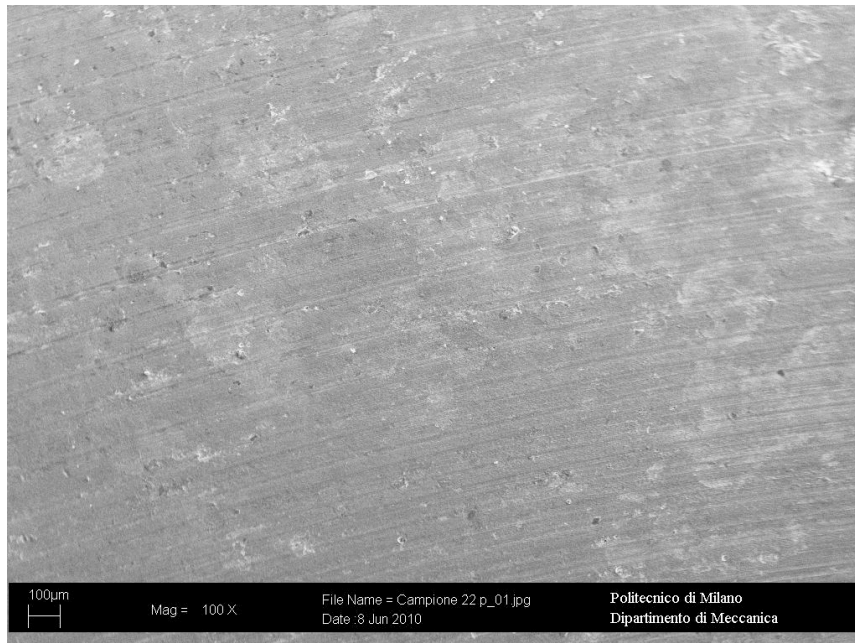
Immagine X100 (SOD=45 mm; f=400 mm/min)
